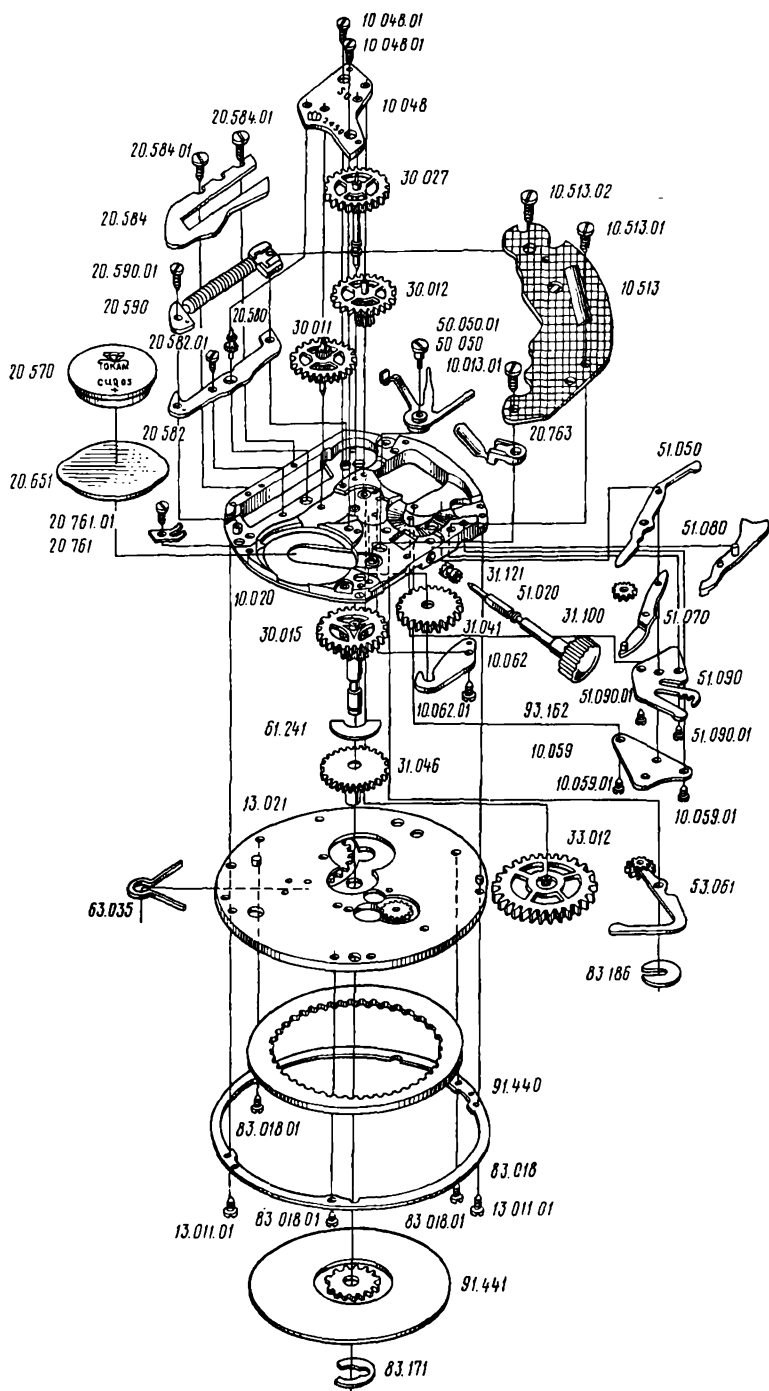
Детали и сборочные единицы механизма часов 2450, 2460:
